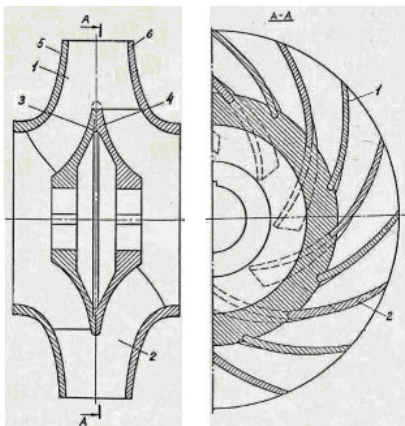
Рабочее колесо сварной конструкции
